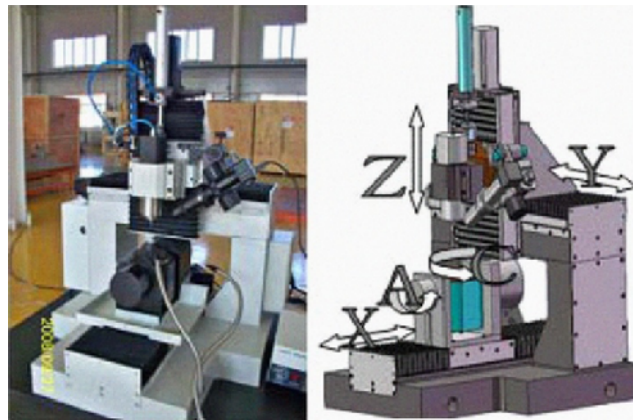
Micromáquina herramienta fresadora de 5 ejes [33].
